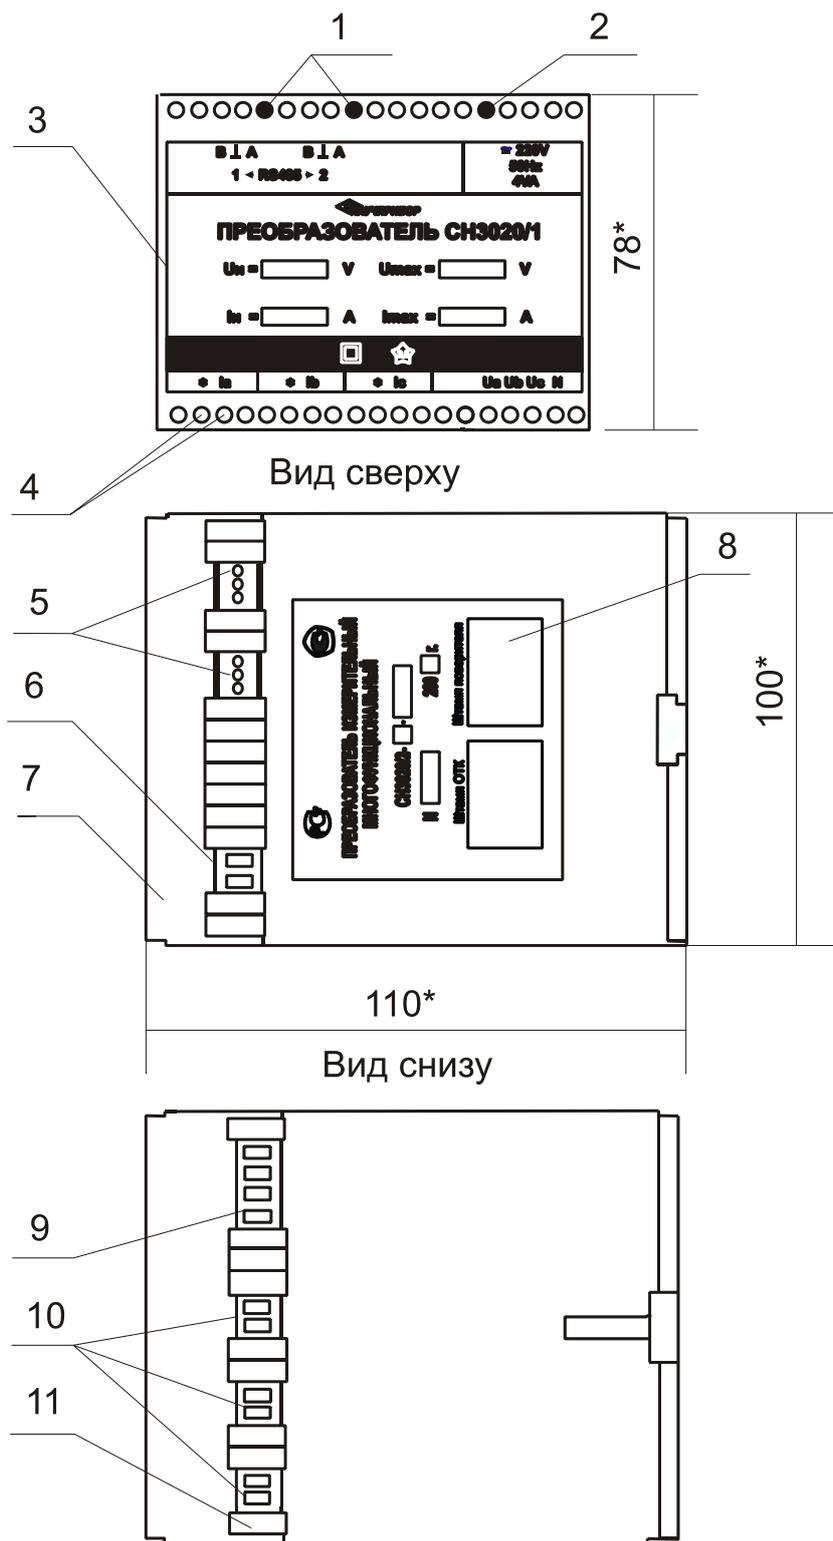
Чертеж внешнего вида преобразователя CH3020
